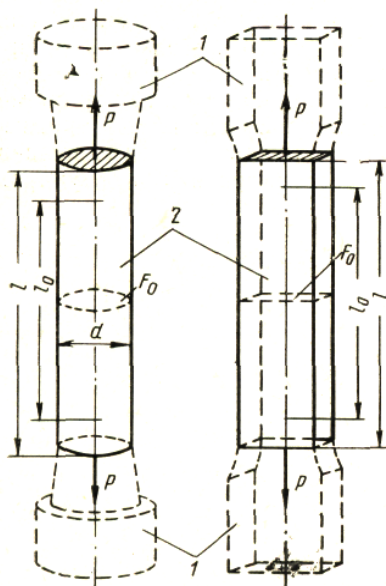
Зразки для випробування розтягування: 1- головки; 2 - робоча частина
